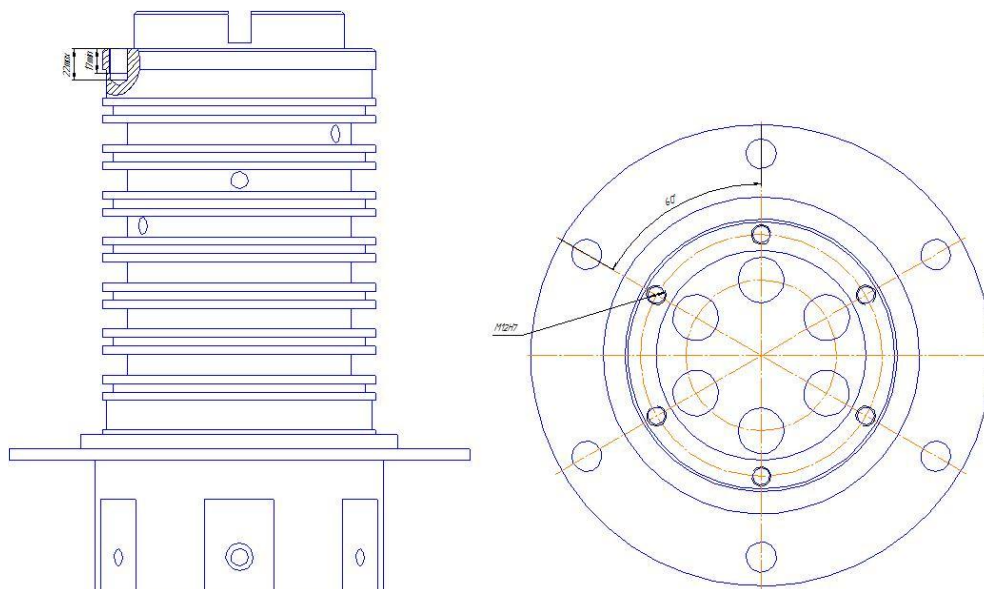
Схема установки детали для горизонтально-сверлильной операции 015
